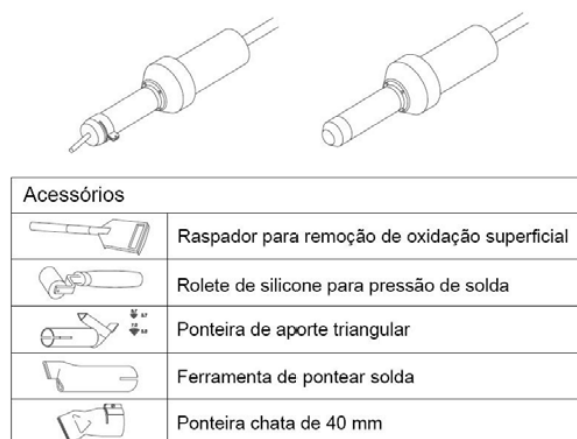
Acessórios utilizados na execução de soldadura por termofusão com recurso a máquina de ar quente (Neoplastic).
